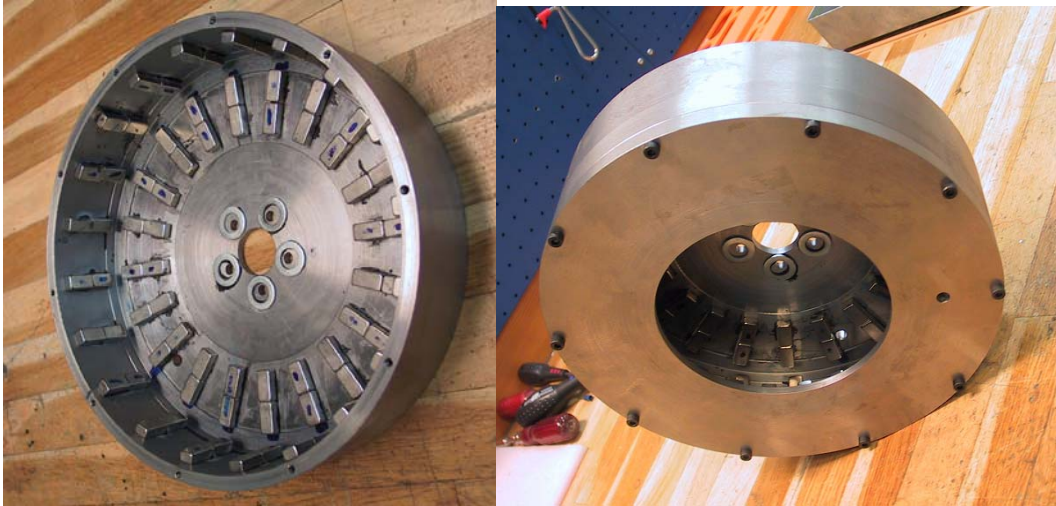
Framstycke med pålimmade magneter och hela rotorn hopskruvad.
